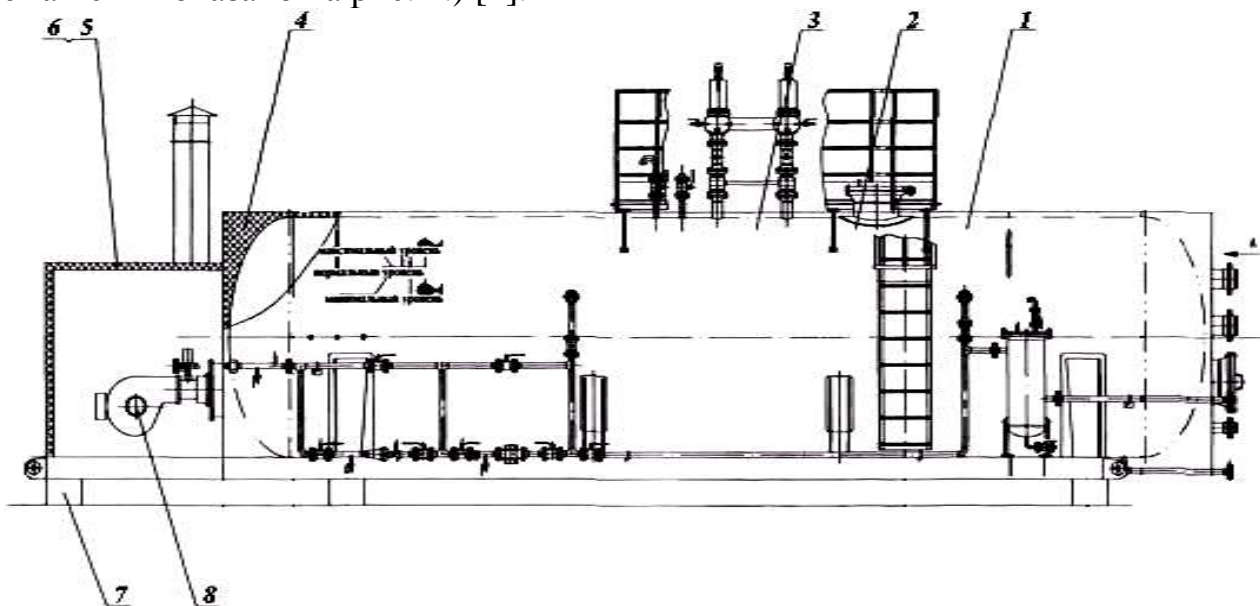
Схема нагревательной печи НЈ2300-Н/1.6-Q с жаровой трубой.
